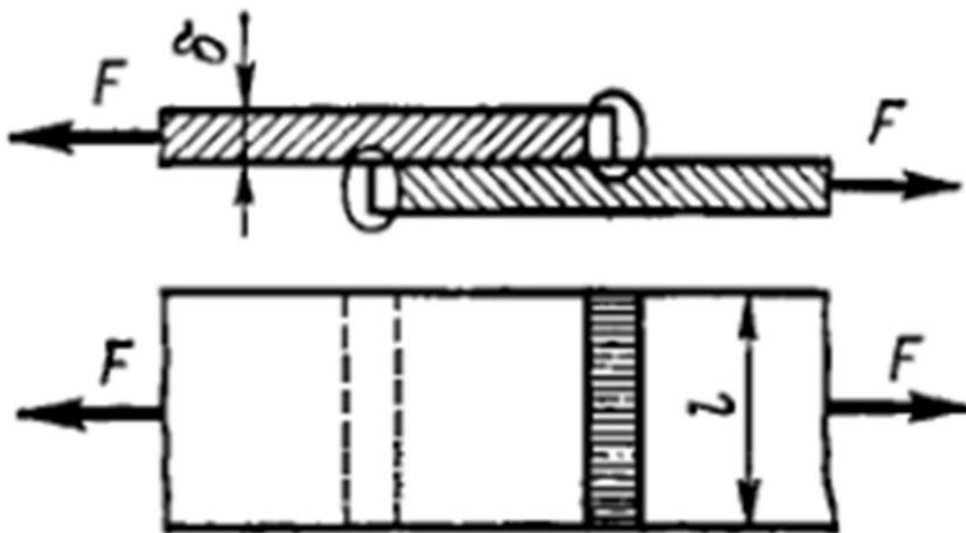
Розтягуючі сили в зварному з'єднанні
